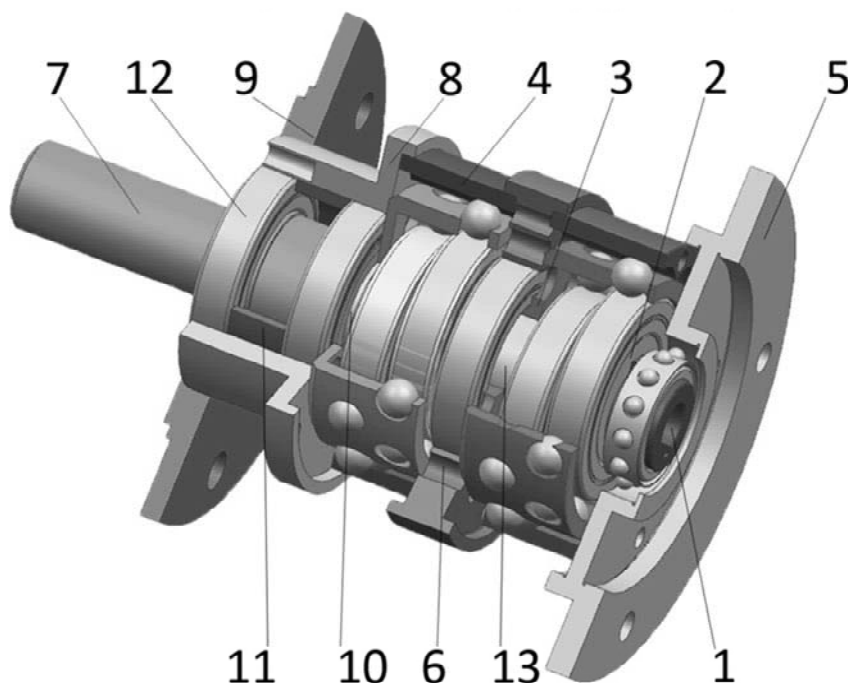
3D-модель двухступенчатого планетарного радиально-плунжерного редуктора
